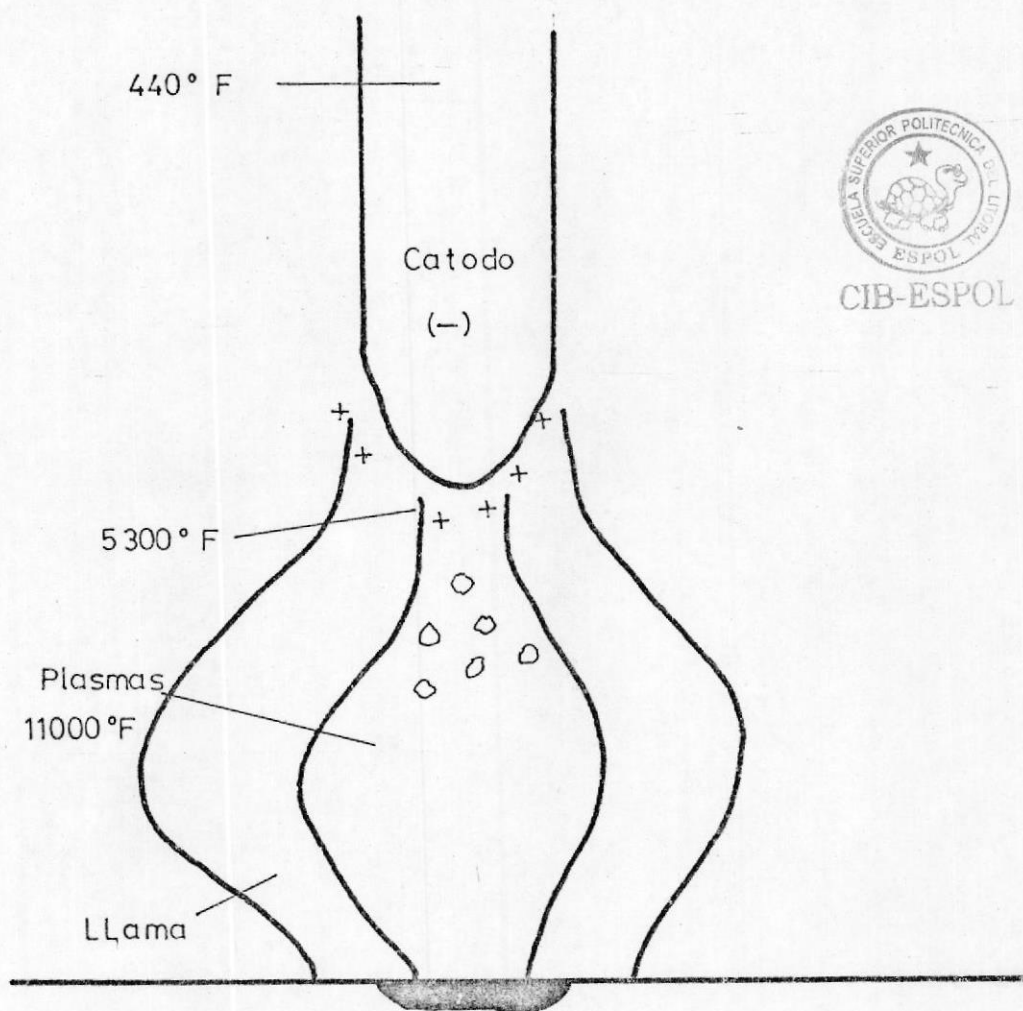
ARCO DE SOLDADURA ELECTRICO (6)
